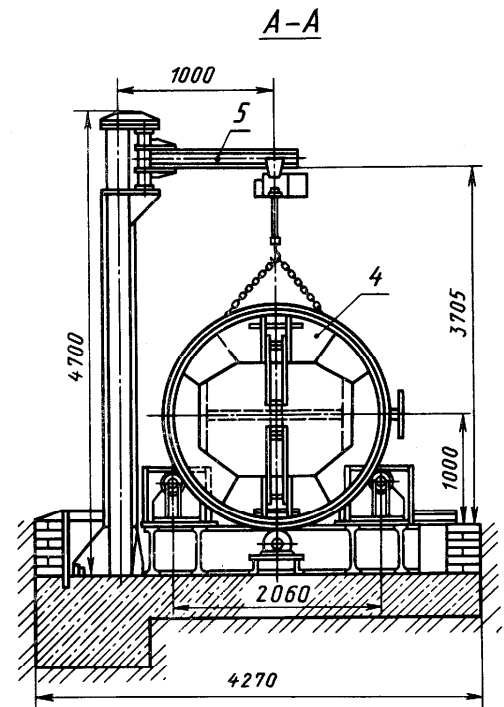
Универсальный кантователь: 1-подвижная опора; 2-зажим; 3-приводной механизм; 4-поворотная шайба; 5-консольный кран
